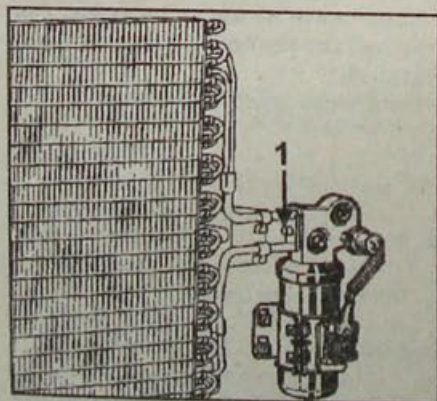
Расположение болта (1) крепления ресивера-осушителя
